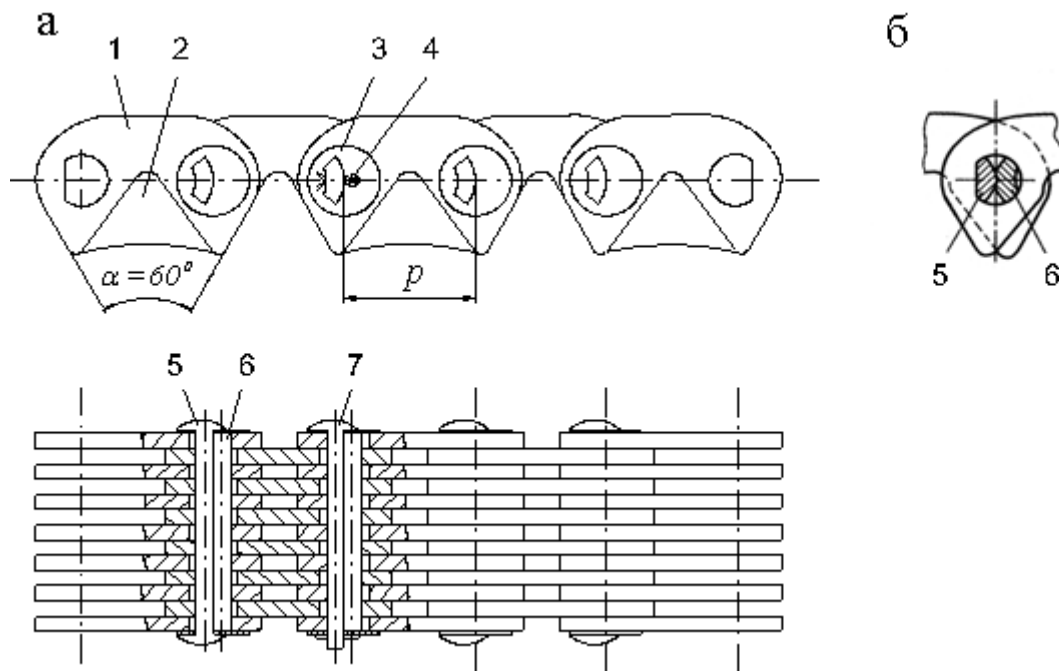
Зубчатая приводная цепь (а) и шарнир качения (б):
